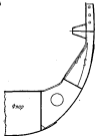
Конструкция сварного соединения шпангоута с двойным дном.
